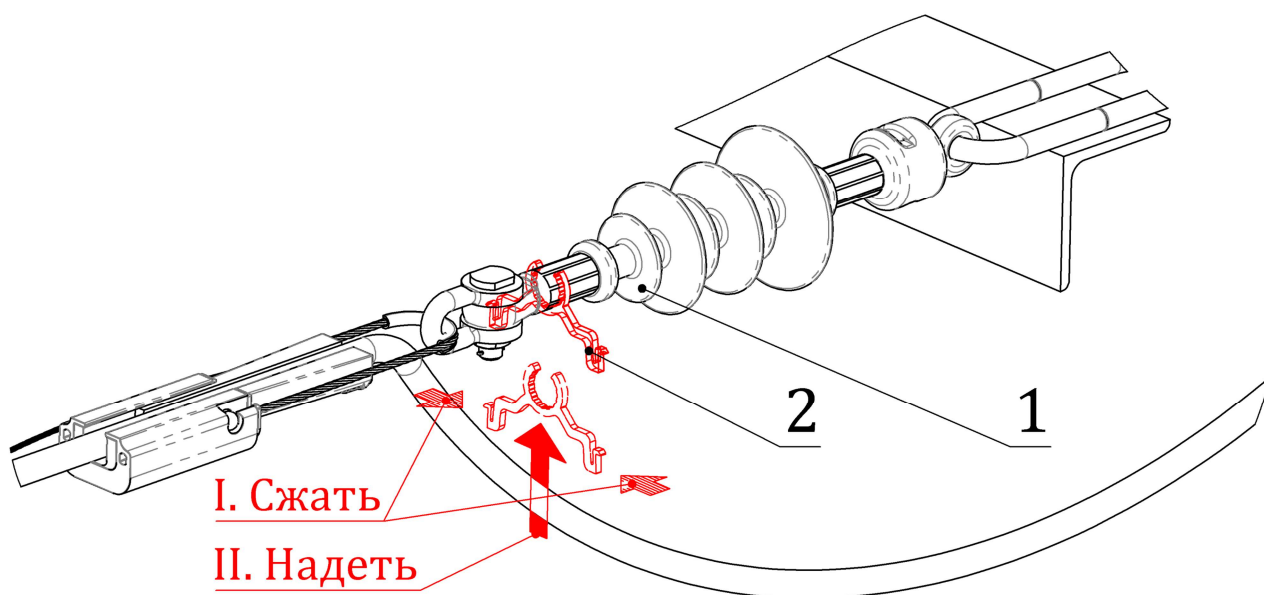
Установка фиксатора ВРА на оконцеватель изолятора
